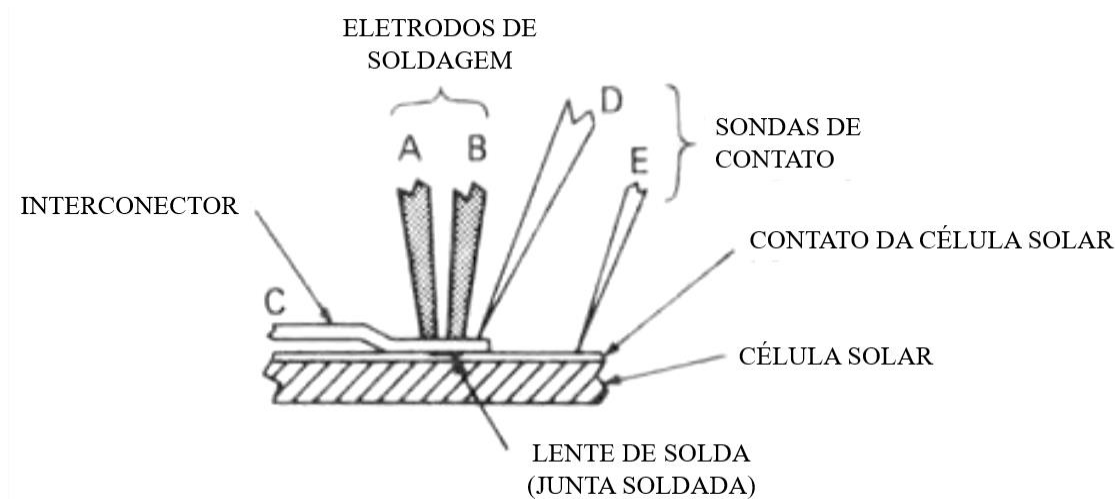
Processo de soldagem por resistência elétrica com eletrodos paralelos. Adaptada de [6].
